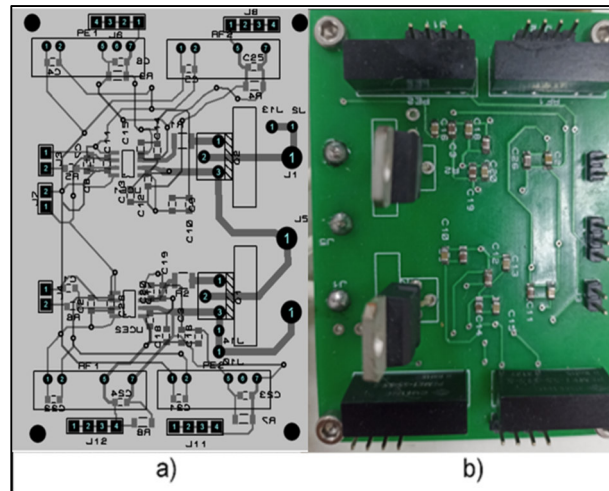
a) Circuito electrónico, b) Placa PCB.
